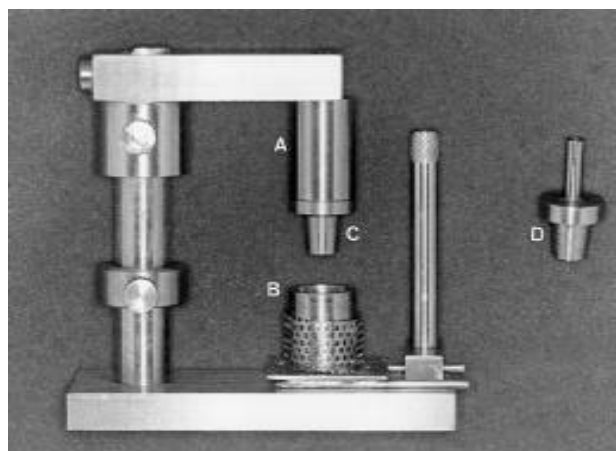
Dispositivo de moldagem contendo: A-) Parte móvel do dispositivo; B-) Posicionador de casquetes; C -) Troquel para moldagem; D -) Troquel para casquetes
